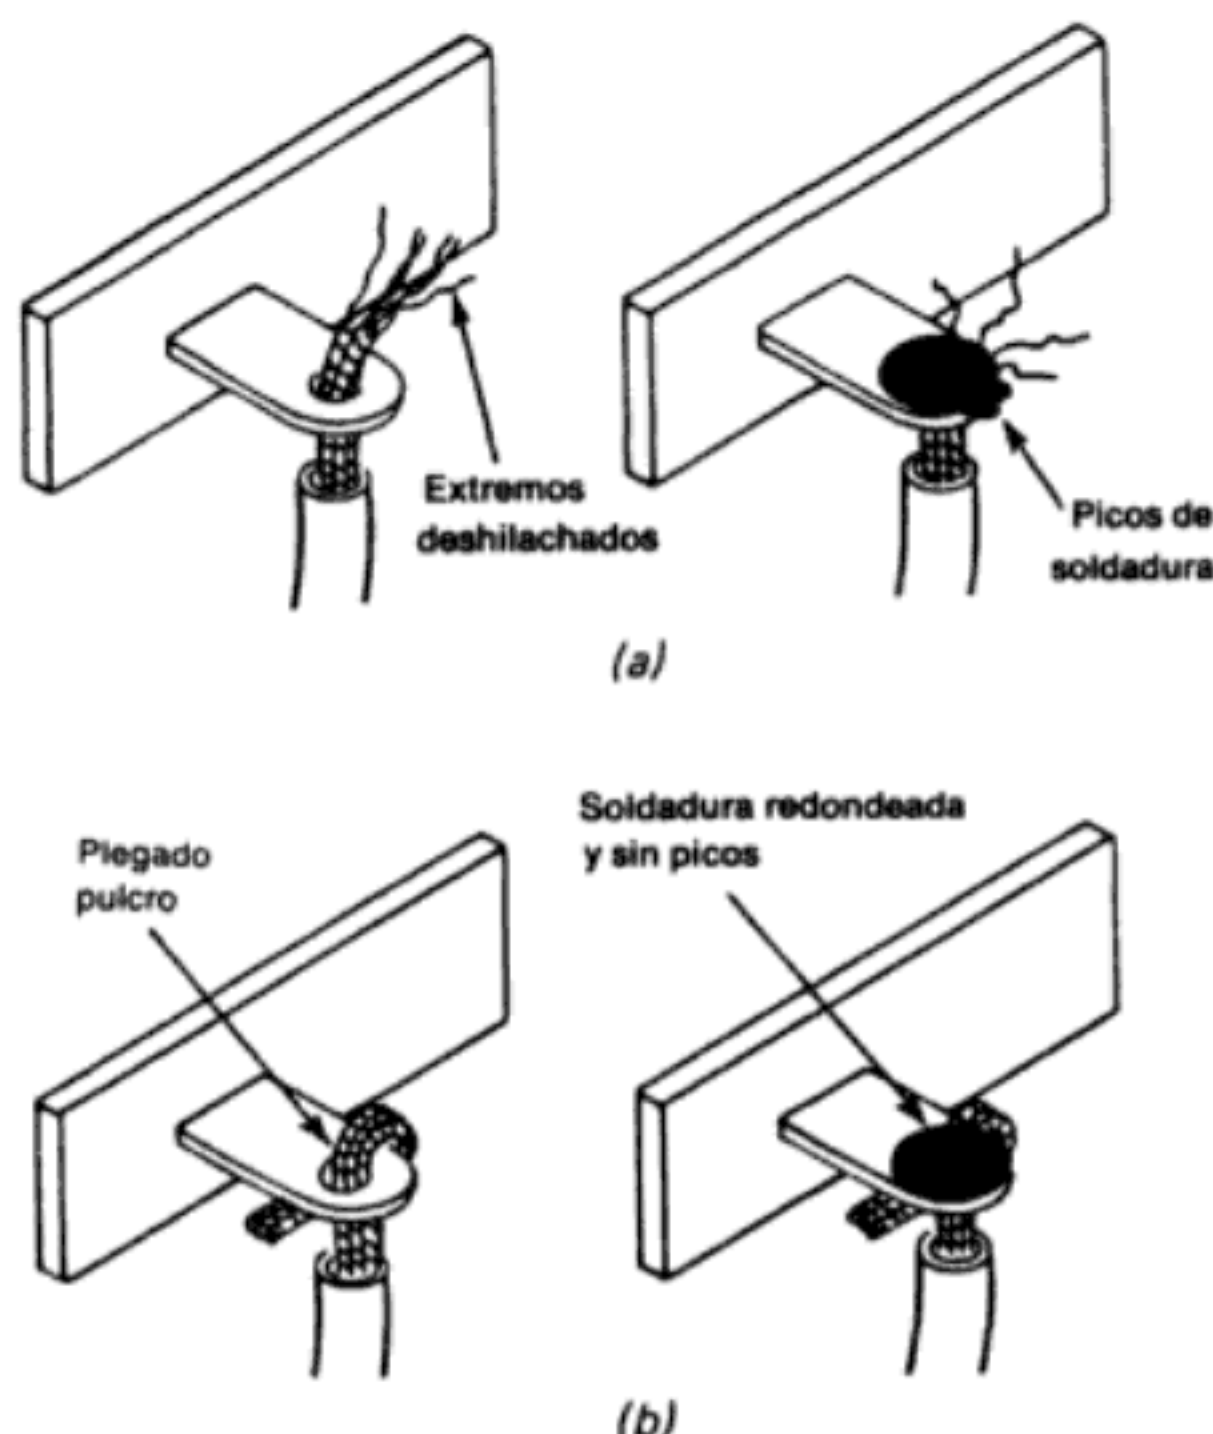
Procedimientos de soldadura. (a) Conexión soldada defectivamente. (b) Conexión soldada bien hecha.
